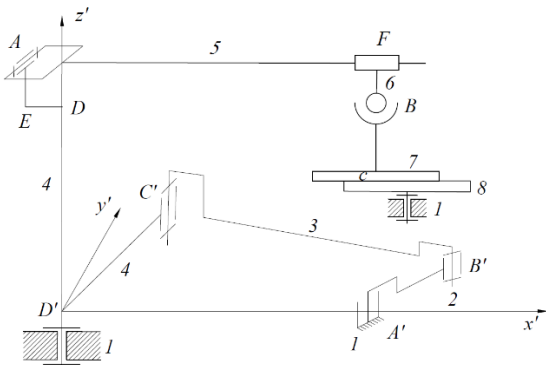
Кинематическая схема исполнительного механизма рычажного станка
